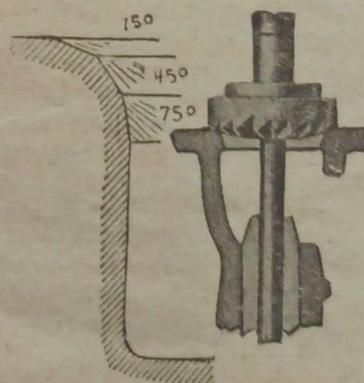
Отделочная фрезер-шарошка для фрезеровки клапан- ных гнезд под углом 15°
